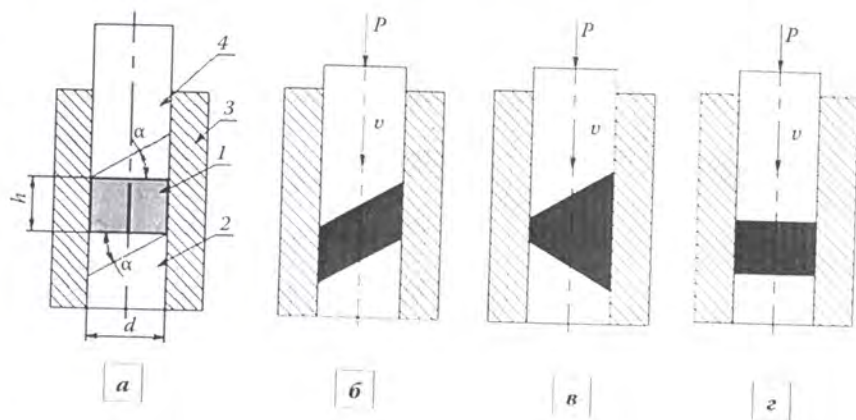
Схема процесса выдавливания угловыми пуансонами: а – исходное состояние; б – 1-й способ; в – 2-й способ; г – калибровка
